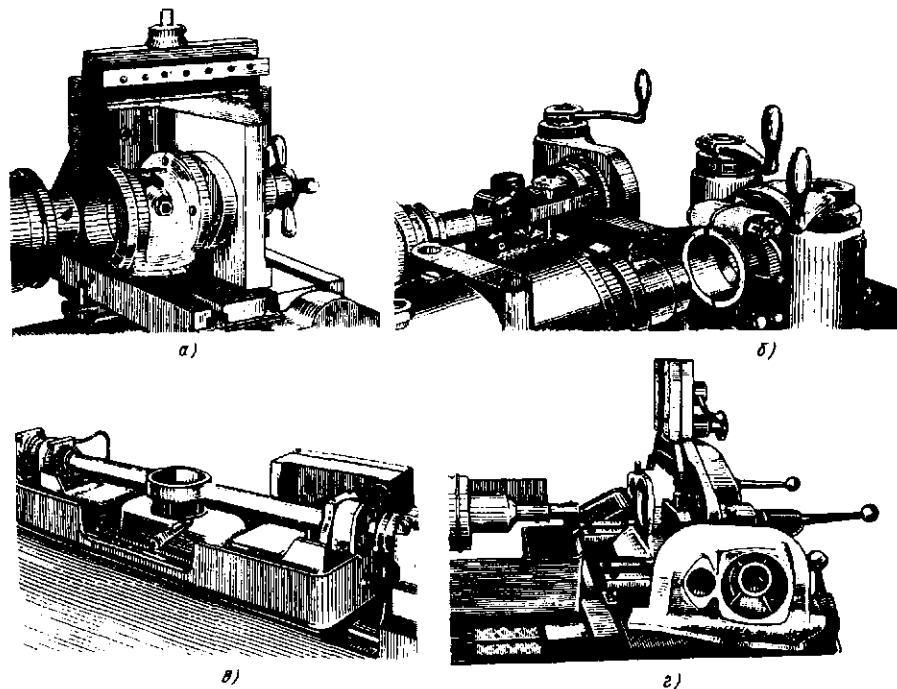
Приспособление для установки и закрепления детали на шпинделе станка
